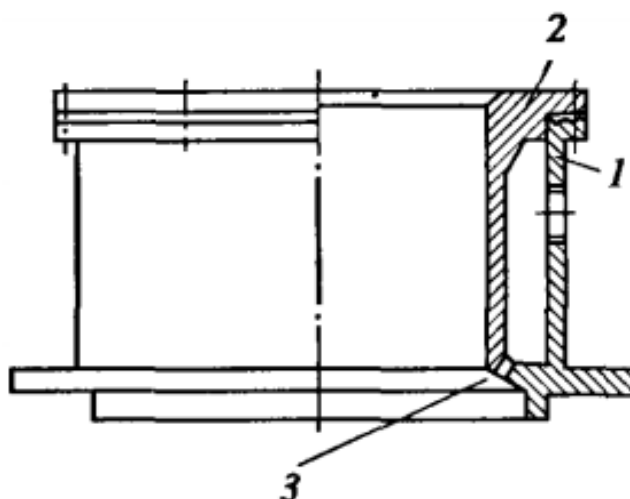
корпусний кристалізатор ковзання для відливки злитків з круглим поперечним перерізом з алюмінієвих сплавів
